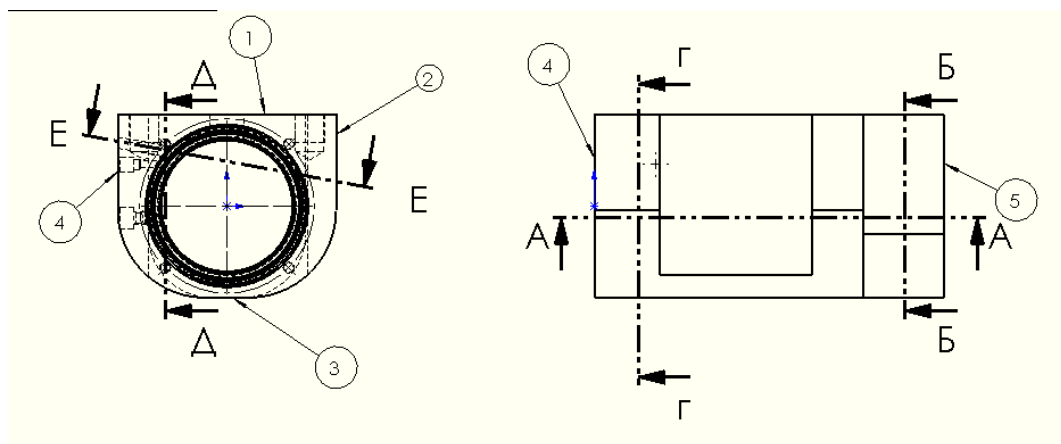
(А) – Ескіз корпусу з нумерацією поверхонь
